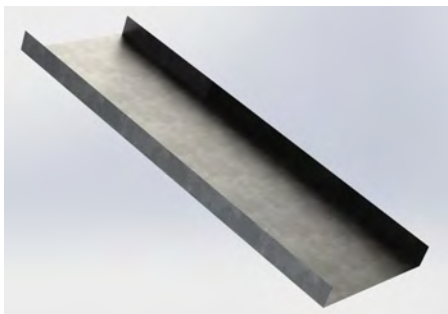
Diseño 3D y ensamblaje del forro de caobilla
